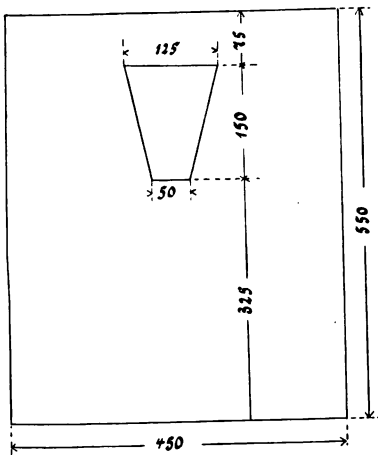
Vorderansicht des Wasserkastens. Die Zahlen geben die Länge in Millimeter an.
